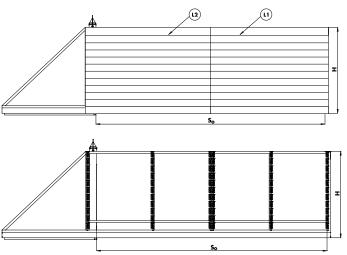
Схема конструкции откатных ворот - горизонтальное заполнение с размещением под углом.
